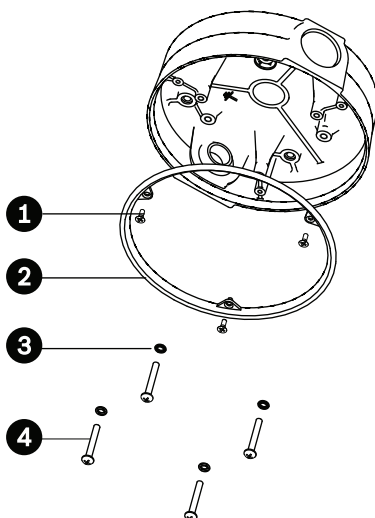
Colocação da junta circular e do anel de retenção para instalação exterior
